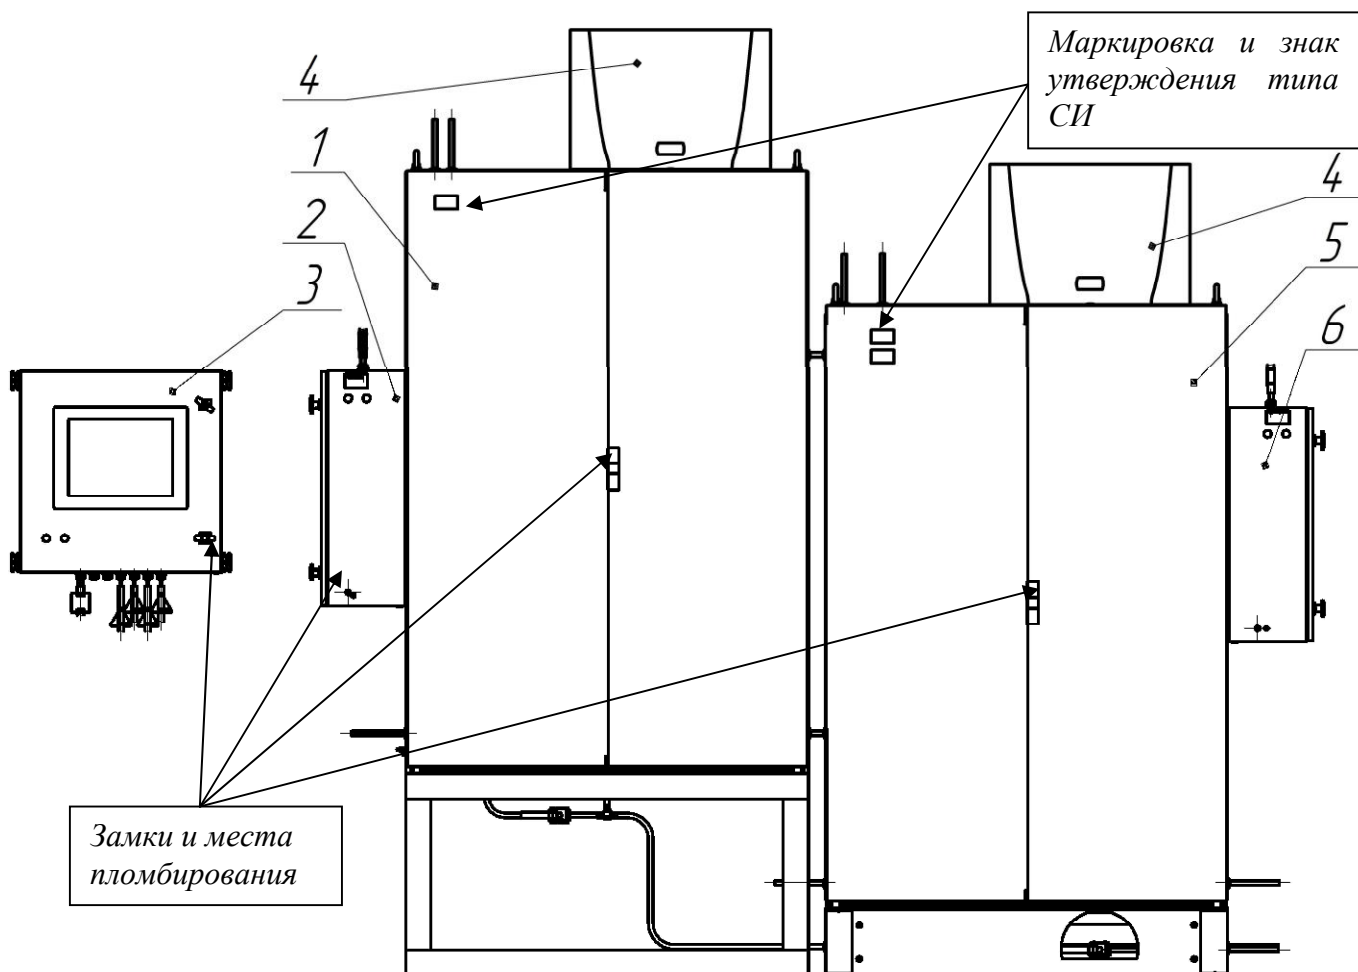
Внешний вид СГЖ и схема пломбировки
